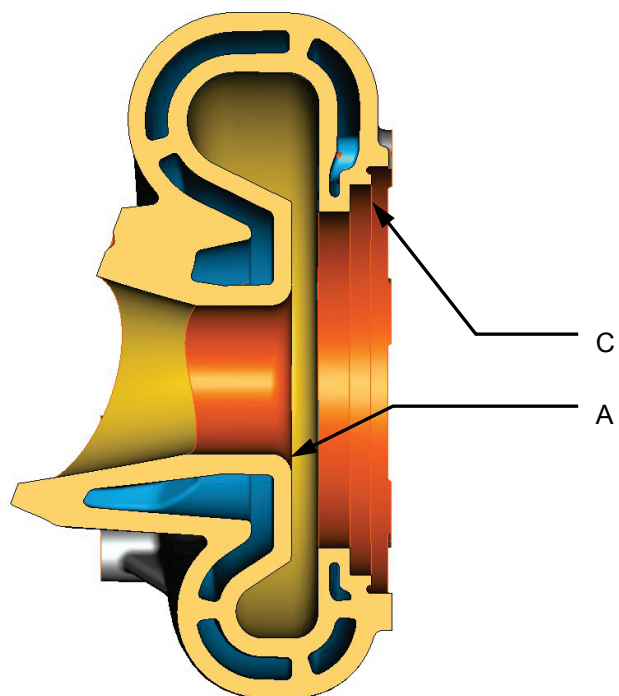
Schnitt durch Turbinengehäuse AVL
